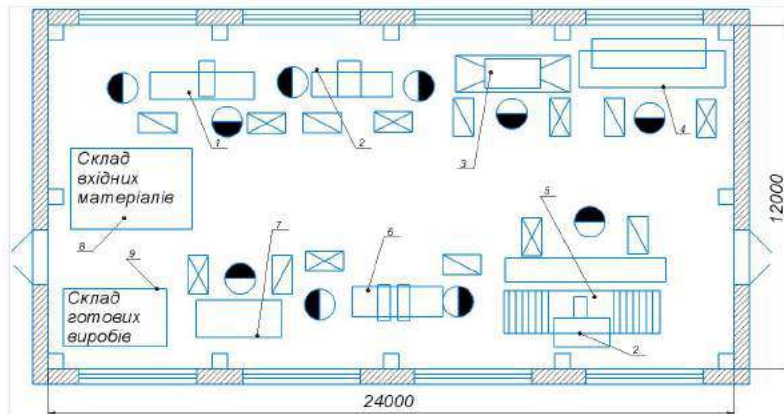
Планування цеху зі створення фасадну №1Рамка-скло
